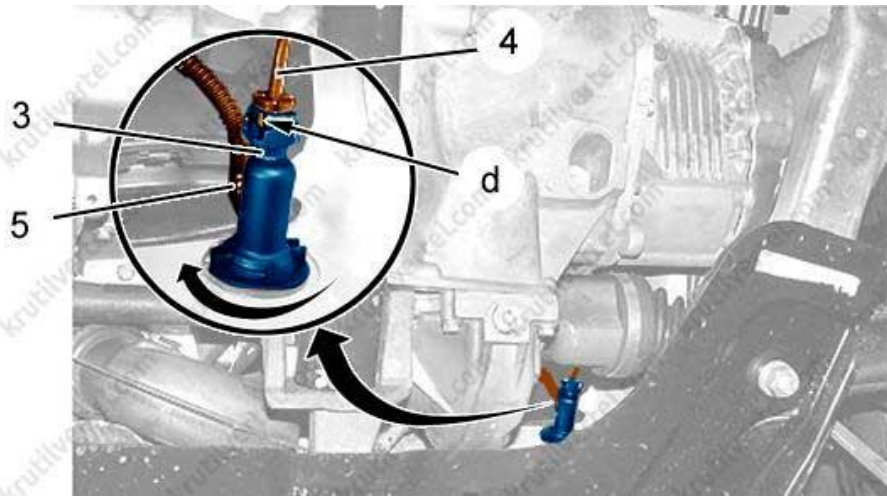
Зняття головного циліндра зчеплення: 3 – корпус циліндра; 4 – подача рідини до робочого циліндра; 5 – подача рідини від бачка.
